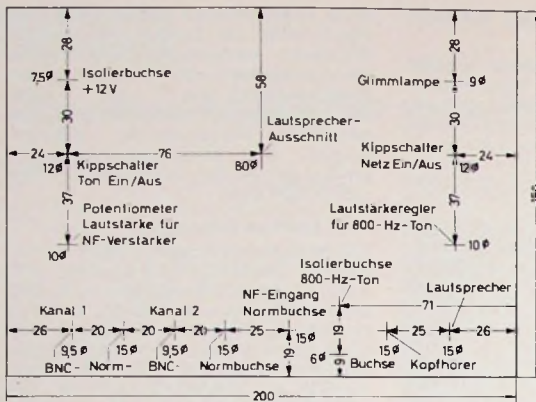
Maßzeichnung des Chassis (nicht maßstabsgetreu gezeichnet)
